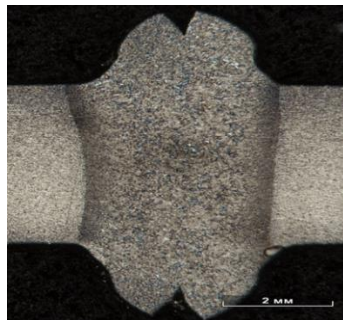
Макрошлиф имитированного сварного соединения двух образцов.
